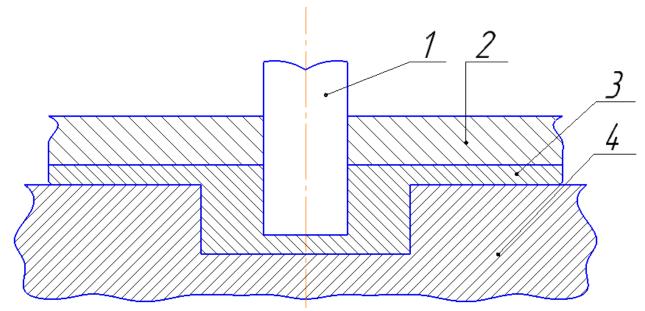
Холодная объемная штамповка в закрытом штампе [6]: 1 – пуансон; 2 – верхний штамп; 3 – тонколистовая заготовка; 4 – нижний штамп
